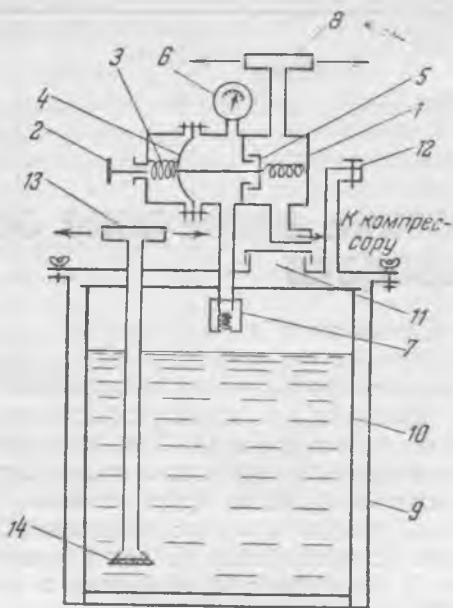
Схематический разрез нагнетательного бачка с редуктором.
